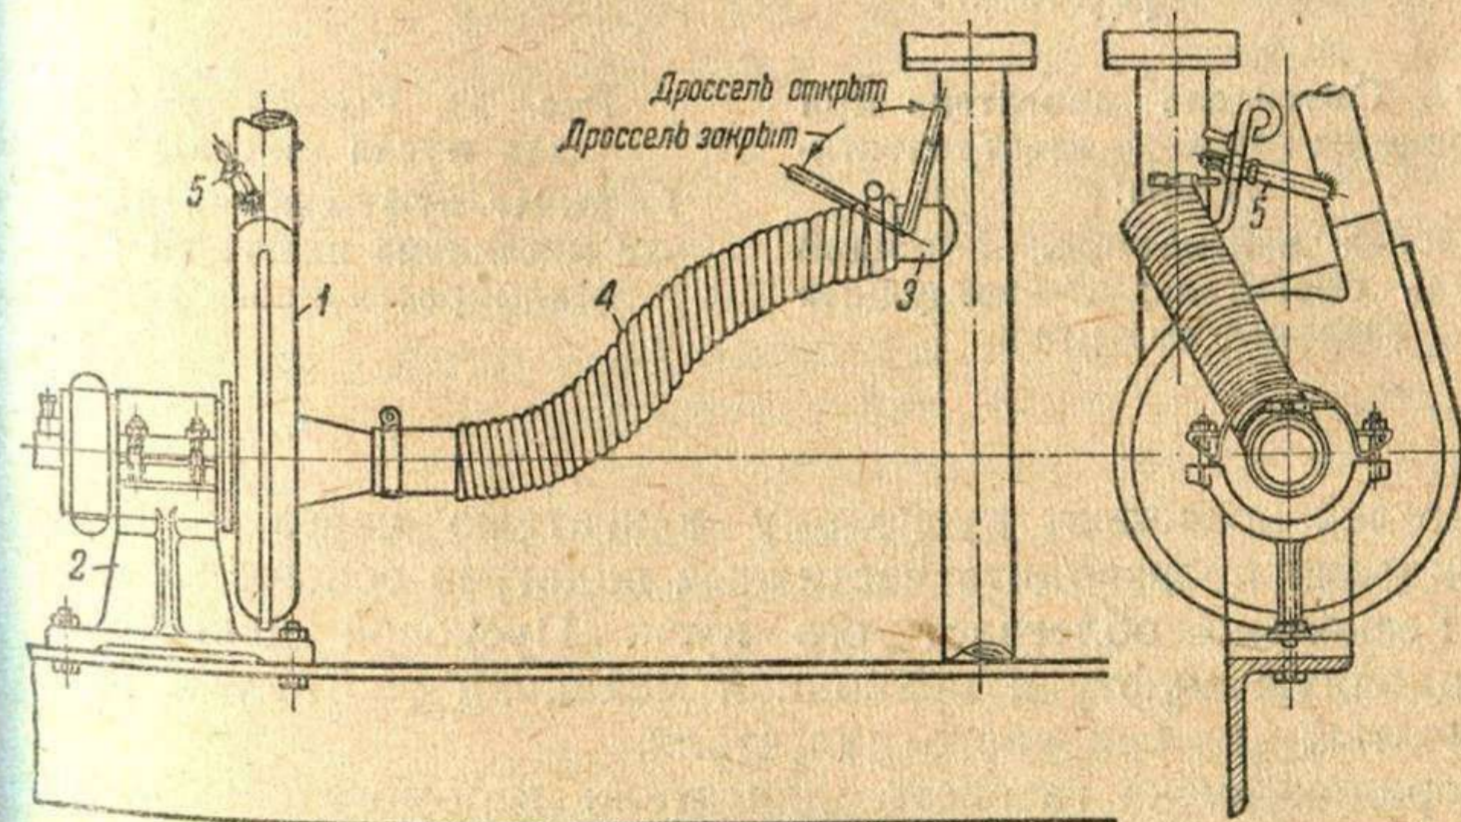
Схема установки ventильатора при стартерном пуске двигателя на газе:
